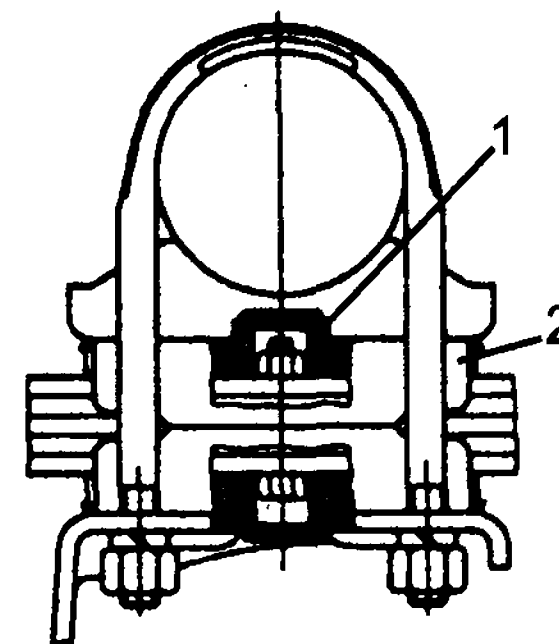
Положение фланцев обоймы рессоры после затяжки гаек стремянок: 1 — подушка; 2 — обойма
